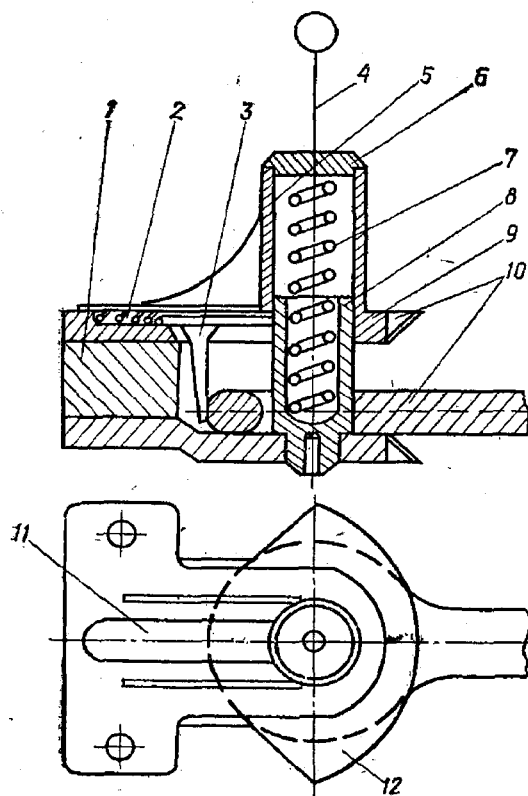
Автозчіпка для трактора: 1 – поперечина; 2 і 7 – пружини; 3 – стопор; 4 – троеик; 5 – напрямник; 6 – накривка; 8 – з'єднувальний палець; 9 – механізм з'єднання; 10 – корпус зчіпки; 11 – крипка; 12 – вловлюван
